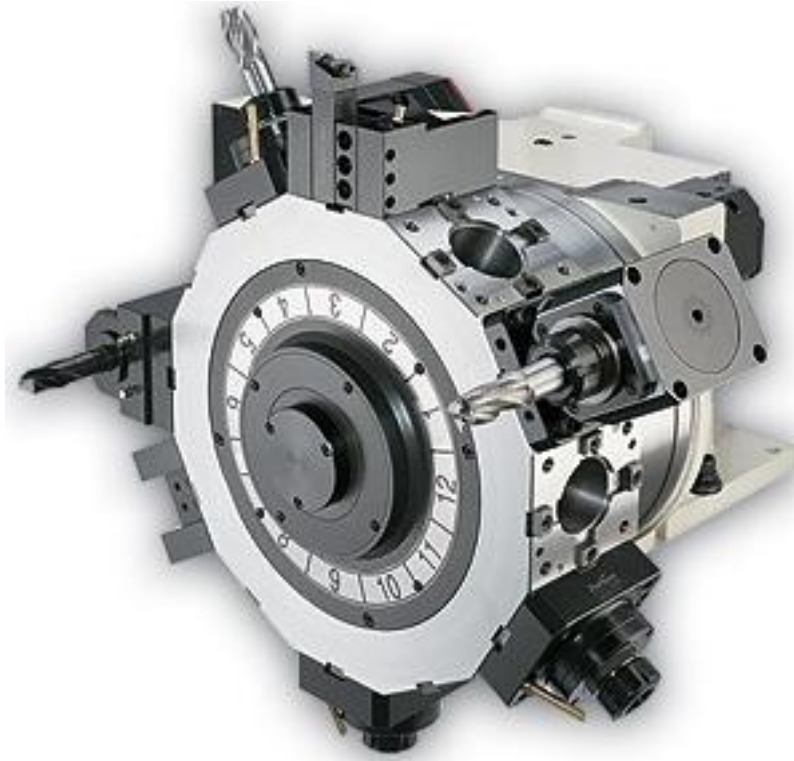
Розміщення приводних інструментів у револьверній головці
